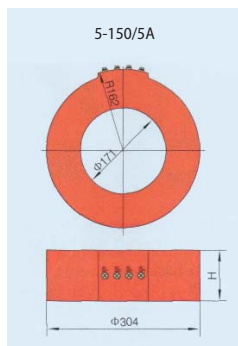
Внешний вид и размеры трансформатора тока LMZH-126
